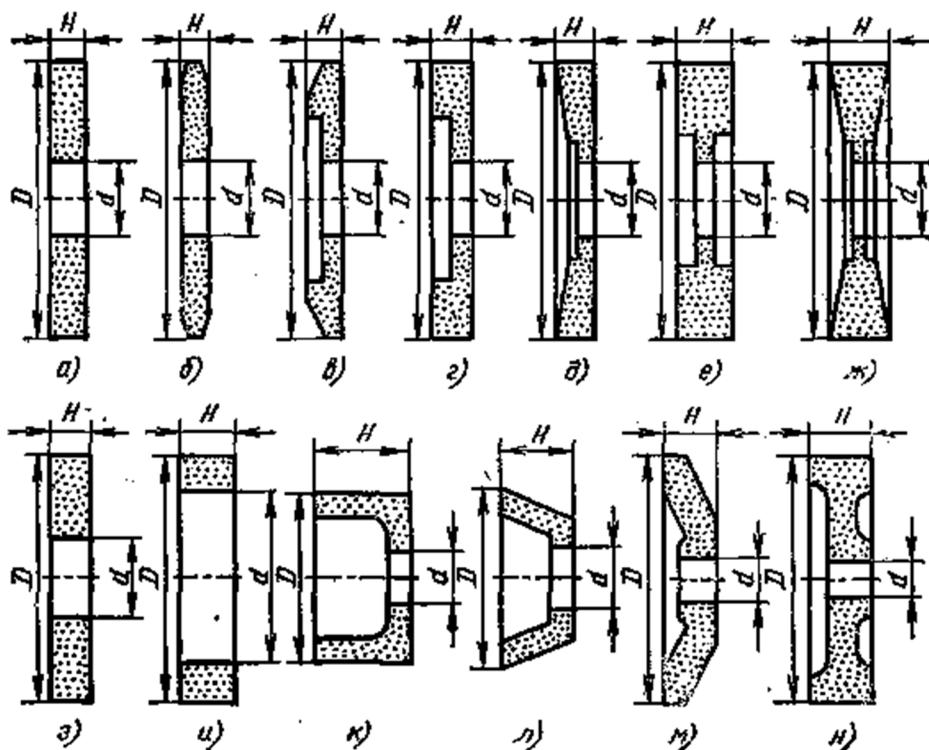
Форма сечений шлифовальных кругов по ГОСТ 2424-83
